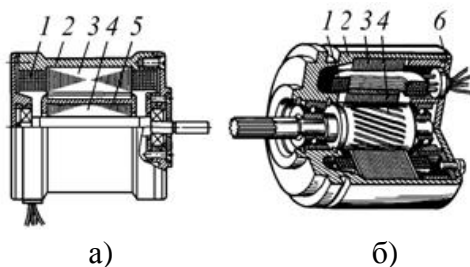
Конструкція виконавчих двигунів (а, б) з «білячою кліткою» на роторі: 1 - обмотка статора; 2 - корпус; 3 - статор; 4 - ротор; 5 - «біляча клітка»; 6 - підшипниковий щит.
